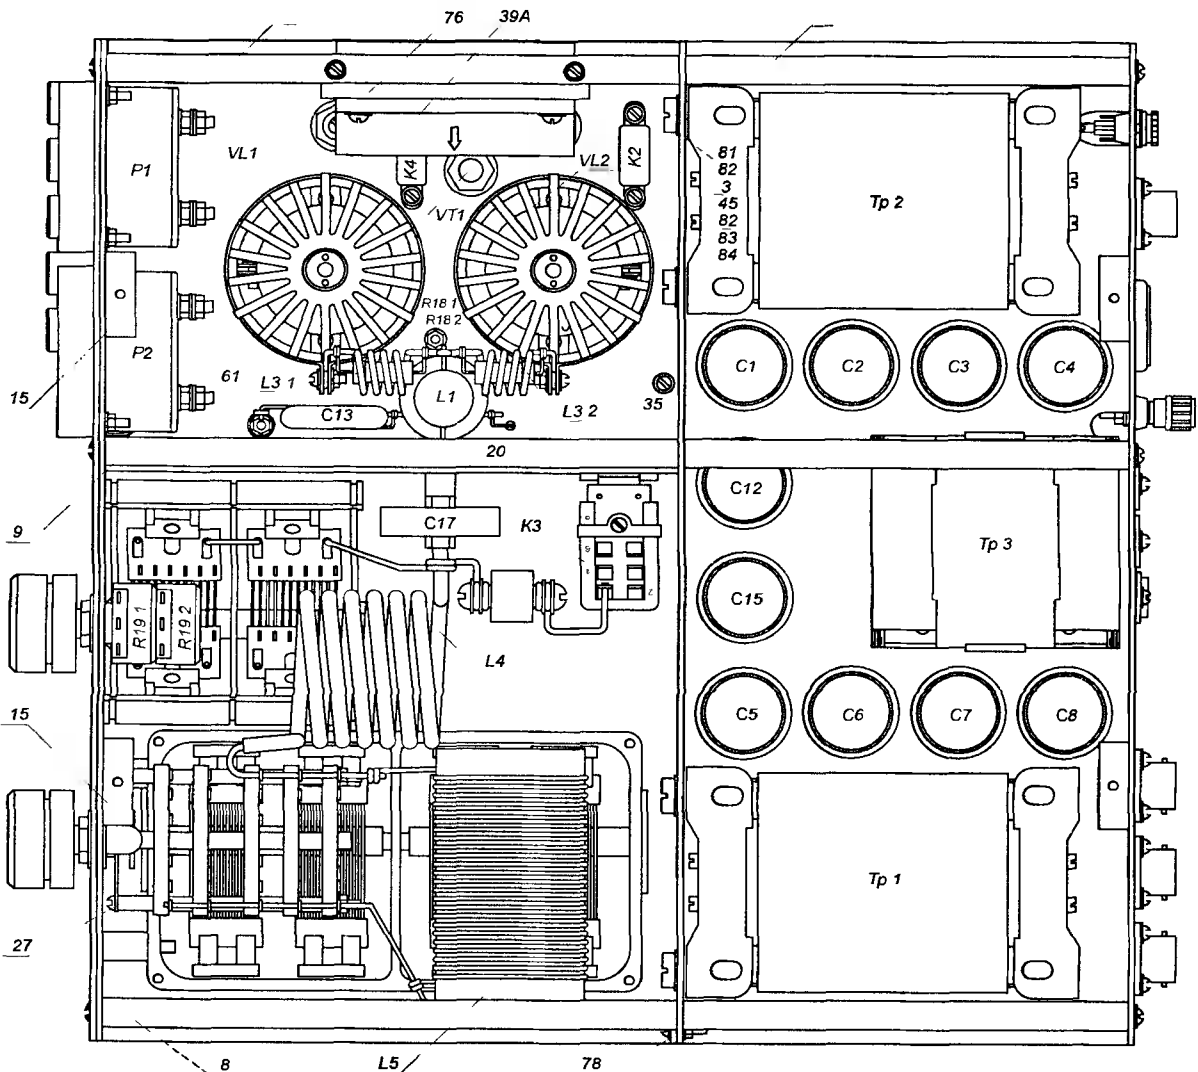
А Сборочный чертеж усилителя DVA 300A. Вид сверху со снятой верхней крышкой
